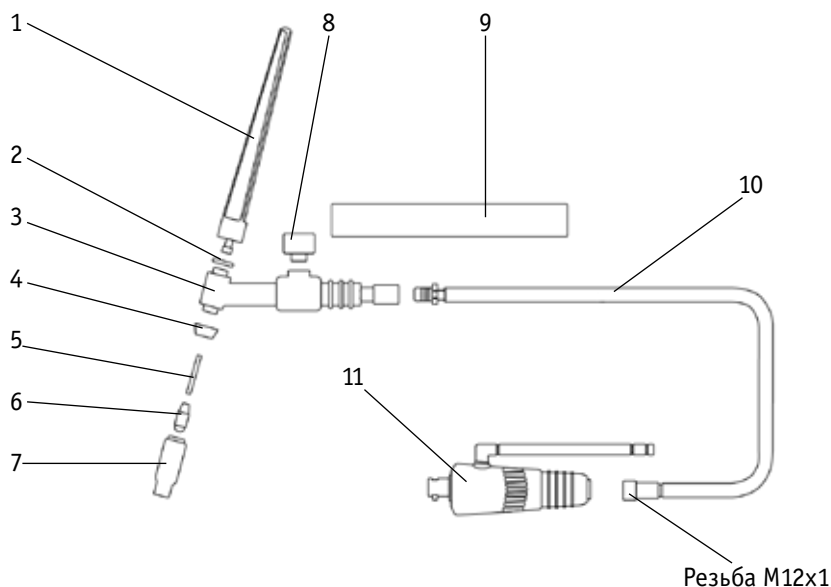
Схема вентильной горелки для аргонодуговой сварки.
